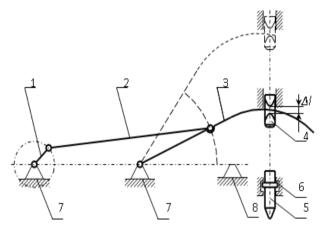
Кинематическая схема ударного механизма переменной структуры с поступательно движущимся бойком
